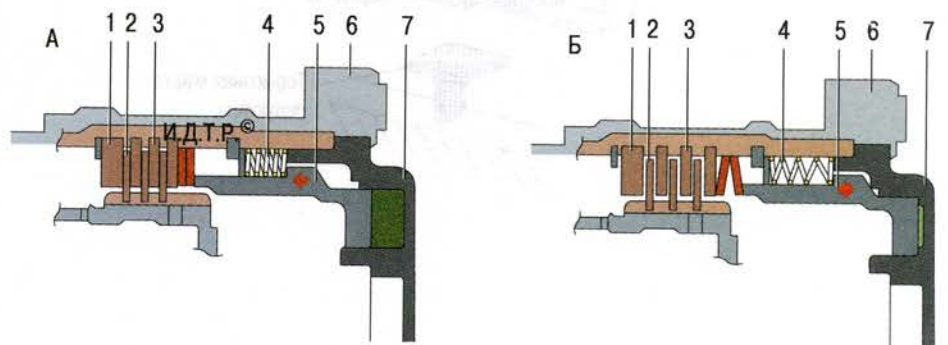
Схема работы дискового тормоза: А – тормоза включены; В – тормоза выключены; 1 – упорный диск; 2 – фрикционные тормозные диски с накладками; 3 – фрикционный диск; 4 – возвратная пружина; 5 – поршень; 6 – картер коробки передач; 7 – крышка картера коробки передач
